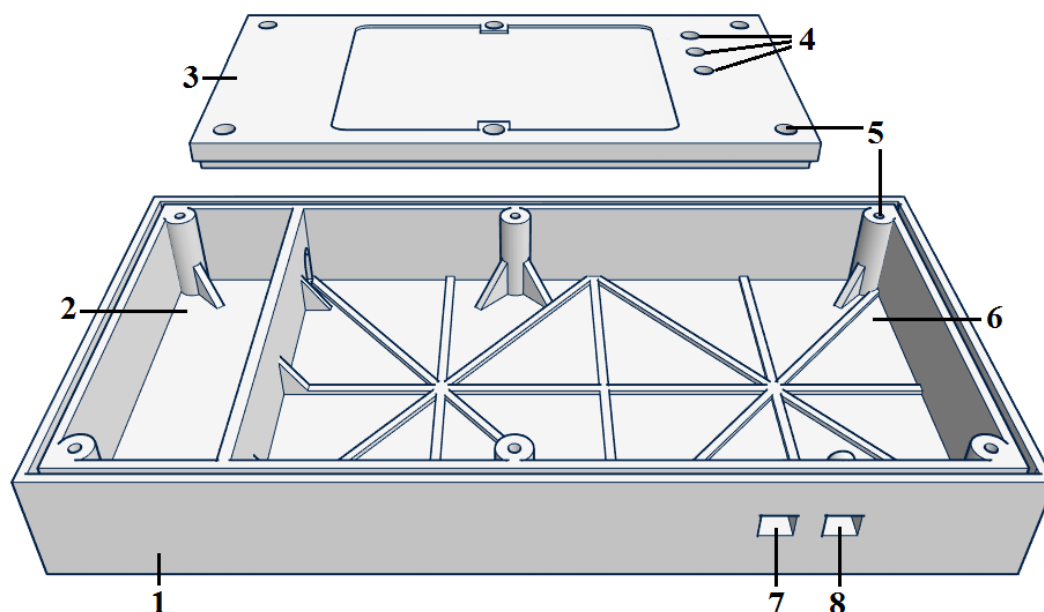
Корпус прибора для проверки датчиков Д-20:
